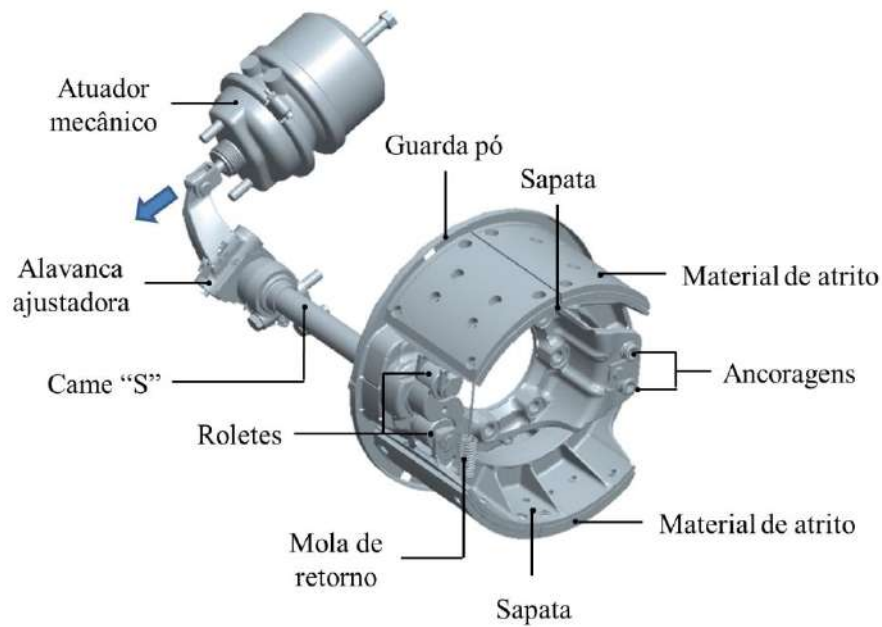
Configuração Típica de um Freio a Tambor do Tipo S-came. Em Destaque os seus Subcomponentes Principais
